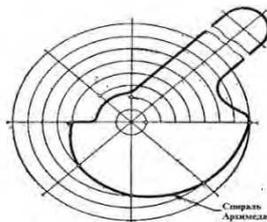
Контур эксцентриковой рукоятки приспособления для зажима деталей, выполненный с помощью спирали
